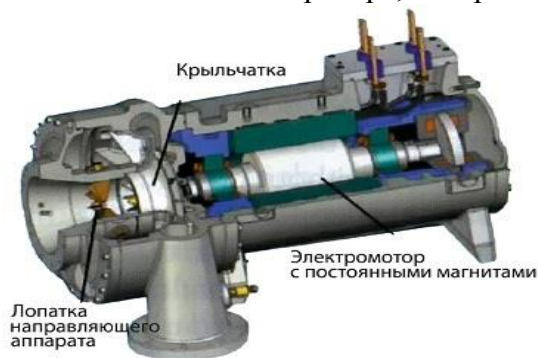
Центробежный компрессор с магнитным подвесом вала с крыльчаткой и *PM*-мотором, соединенными напрямую
